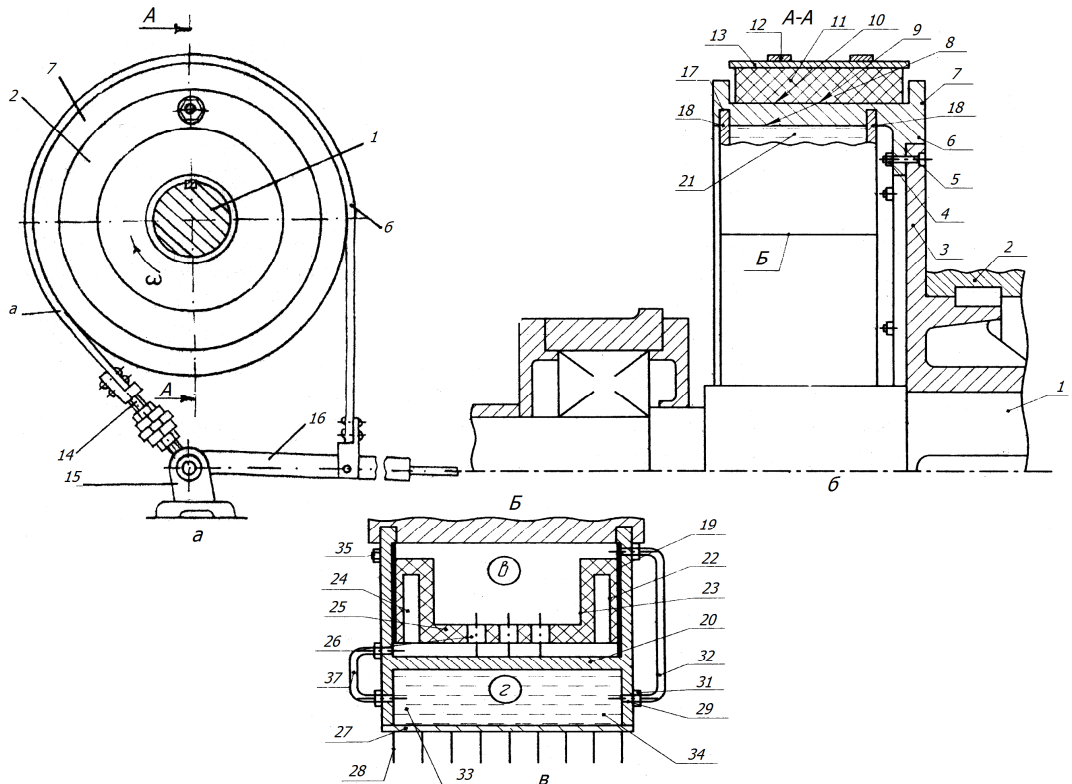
Ленточно-колодочный тормоз с устройством для принудительного охлаждения: *a* – общий вид тормоза; *б* – продольный разрез тормоза по А-А; *в* – вид Б на узлы тепловой трубы: 1 – подъемный вал; 2, 3 – канатный барабан с фланцем; 4 – болтовое соединение; 5, 7, 8 и 9 – выступ, реборды, рабочая и нерабочая поверхности обода тормозного шкива (6); 10, 11, 12 – полимерная накладка с рабочей поверхностью и с крепежными усиками; 13 – тормозная лента с набегающей (*a*) и сбегающей (*б*) ветвью; 14 – резьбовая стяжка; 15 – опора; 16 – рычаг управления; 17 – продольные пазы на нерабочей поверхности обода шкива; 18, 19 – боковые стенки с капиллярно-пористой структурой; 20 – кольцевая стенка; 21, 22, 23, 25 – первая кольцевая камера с изделием (капиллярно-пористой структурой) с вертикальными и горизонтальными составляющими; 24 – несквозные пароотводящие каналы; 26 – конденсатоотводящие сквозные отверстия; 27, 8 – вторая кольцевая камера с оребрением; 29, 30 – сквозные отверстия с резьбой; 31, 32, 33 – штуцера паропроводов и конденсатопроводов; 34 – теплоноситель; 35 – обратный клапан
